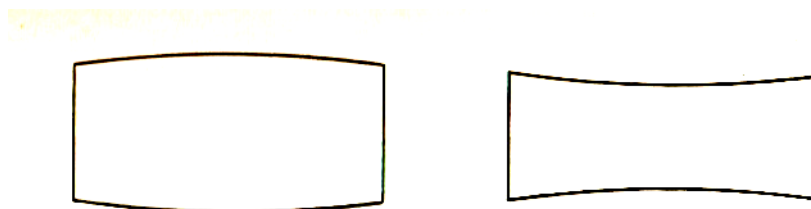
Efecto positivo (izquierda) y efecto negativo (derecha) del barrilamiento
